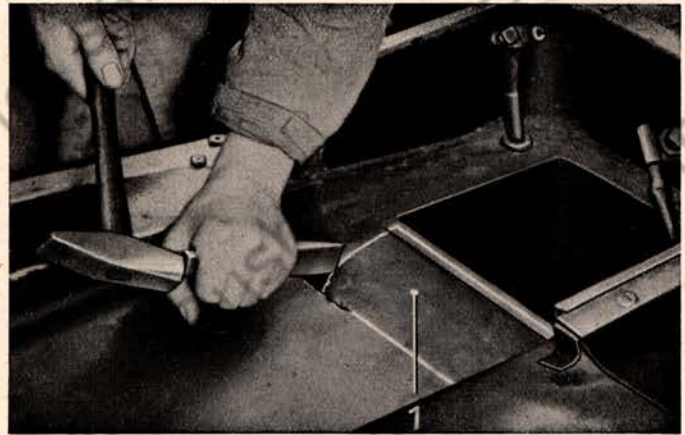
Ausschnitt im Bodenblech des Sammlerkastens
